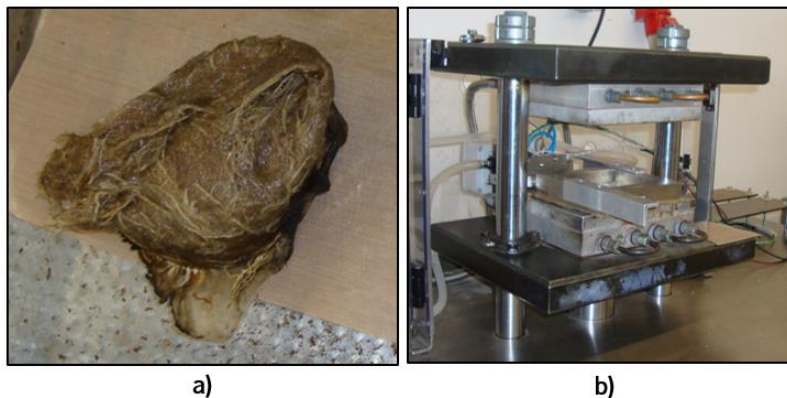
Composto extraído da câmara de mistura (a) e colocado de seguida na cavidade do molde (b)
